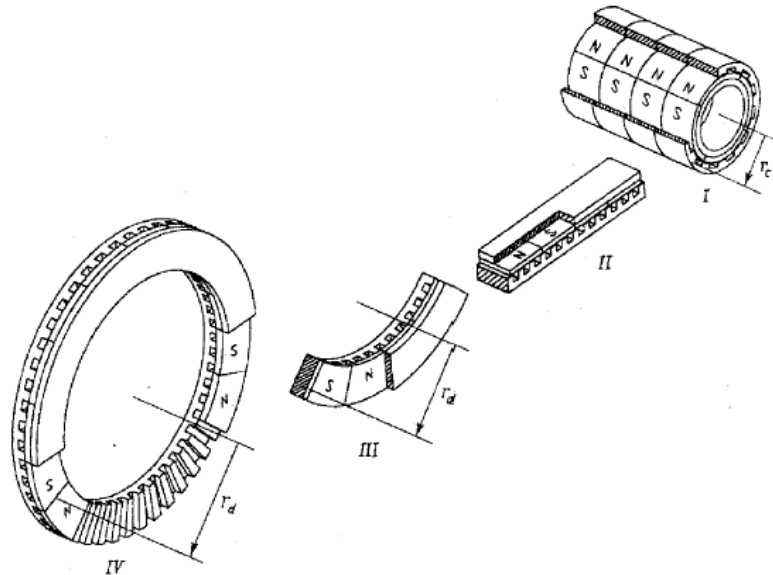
Переход от цилиндрической конструкции к дисковой
